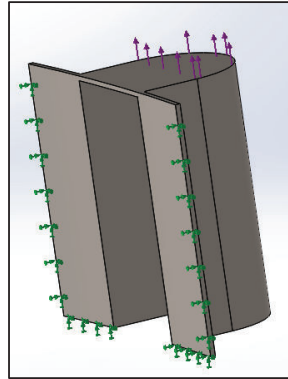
47 Restricciones y Cargas aplicadas a la unidad
